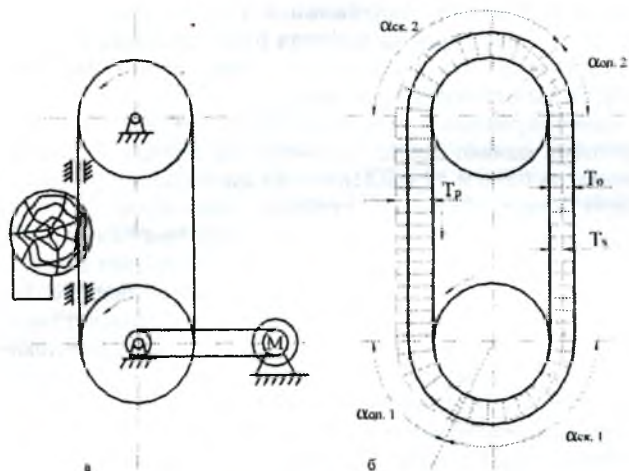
Схема устройства механизма резания ленточнопильного станка:
